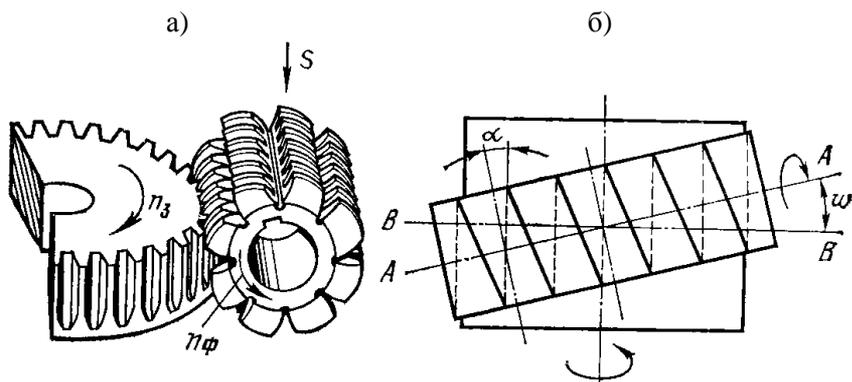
Схема нарезания зубчатых колес червячной фрезой
